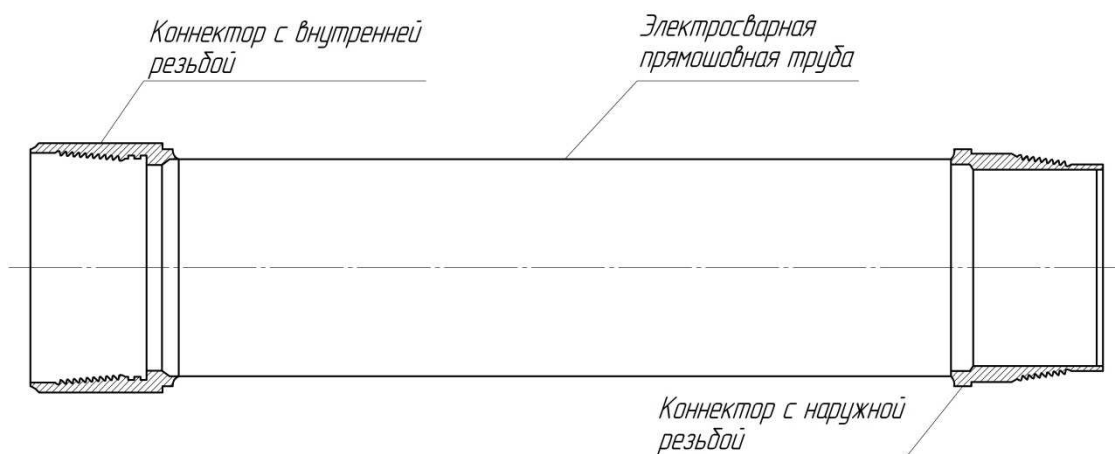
Схема кондукторной трубы с приваренными коннекторами
